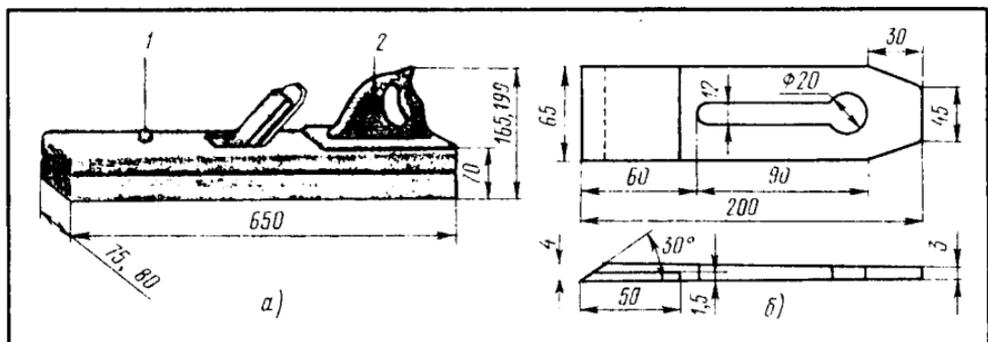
Фуганок: а — общий вид, б — нож фуганка; 1 — пробка, 2 — ручка
